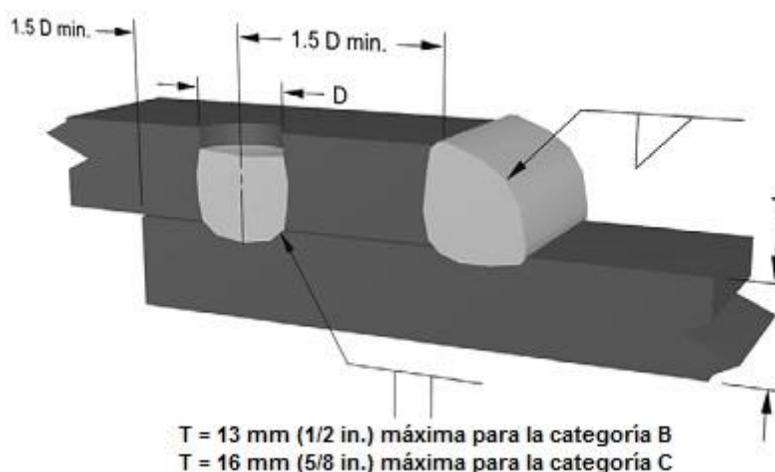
Unión por soldadura de tipo 5.
